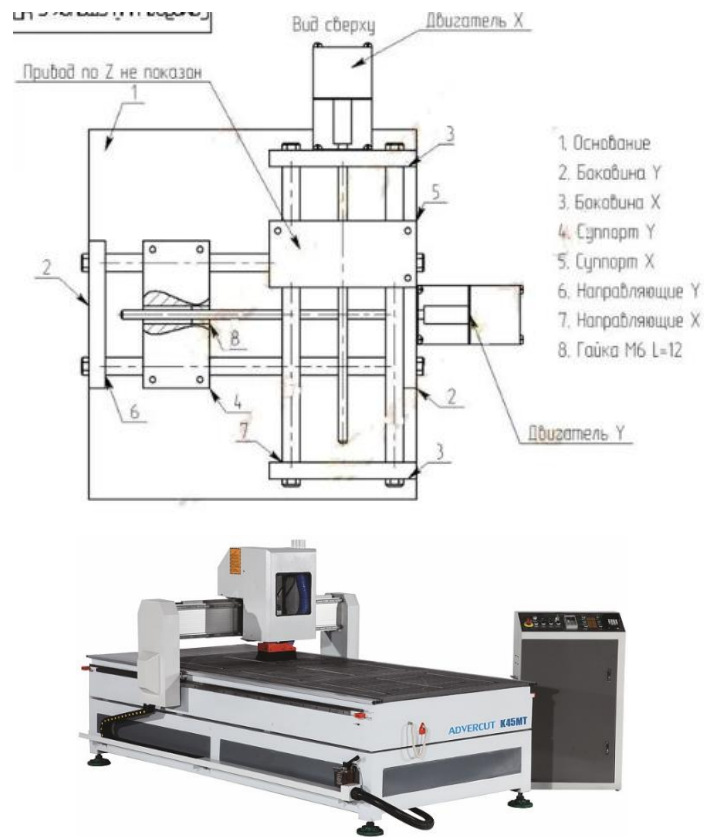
3д-фрезерний станок з ЧПУ
